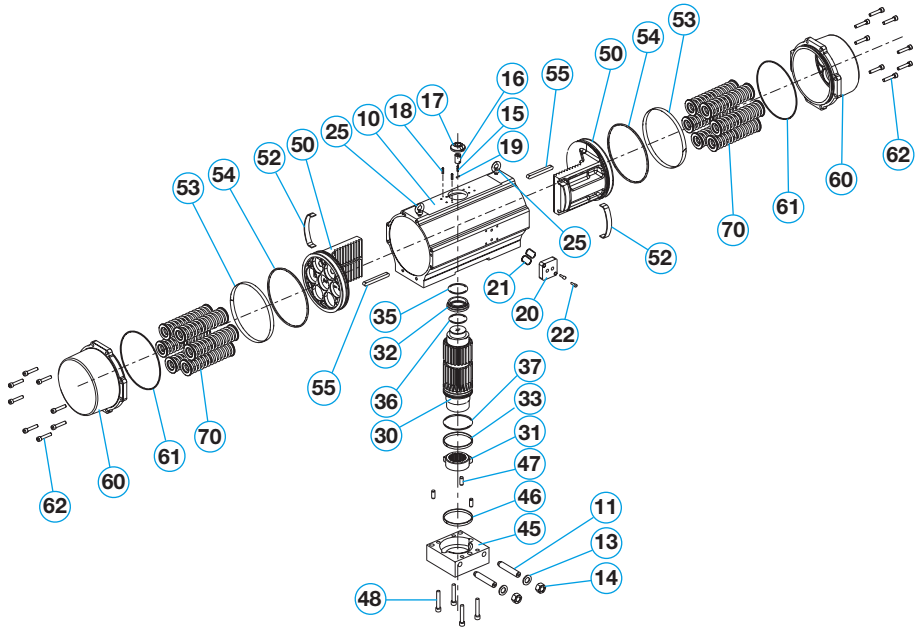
Explosionszeichnung aller Einzelkomponenten Schwenkantrieb actubar
